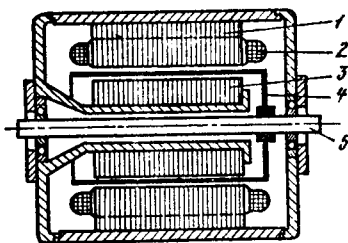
Схема конструкции исполнительного двигателя с полым немагнитным ротором
